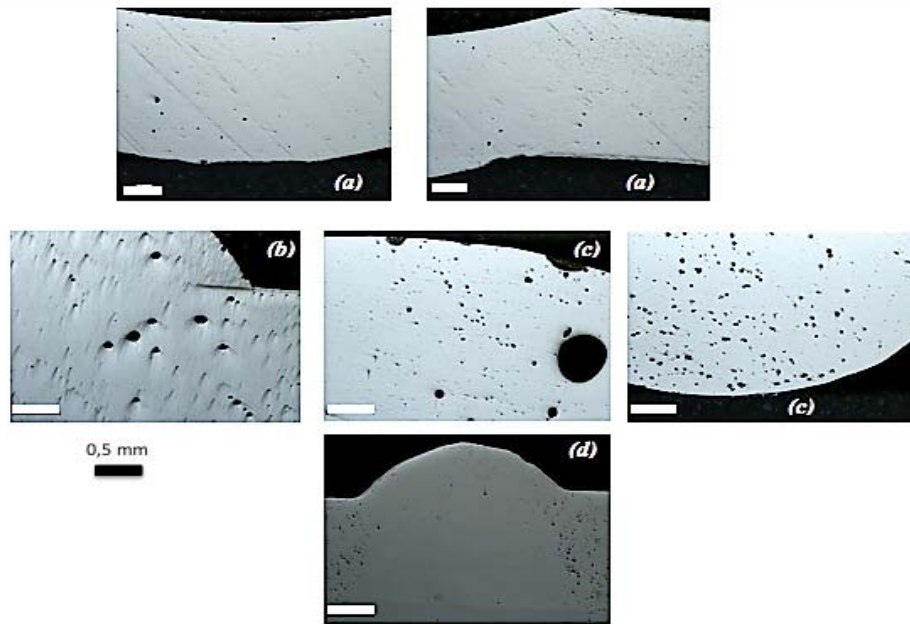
Etat de surface d'un polissage d'un joint soudé avant attaque chimique.
